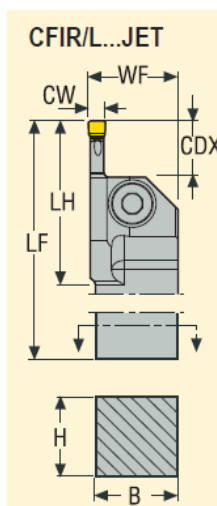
Державка резца для прорезания канавки на валу К-12-11
